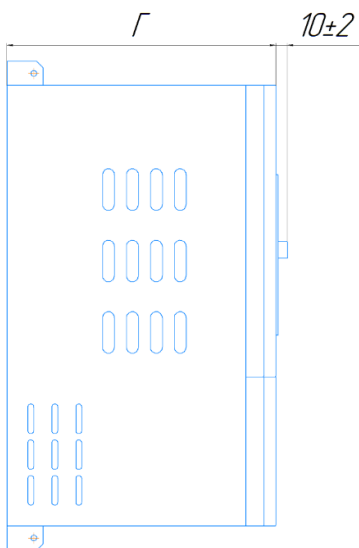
а – габаритные и установочные размеры LCI в металлическом корпусе
